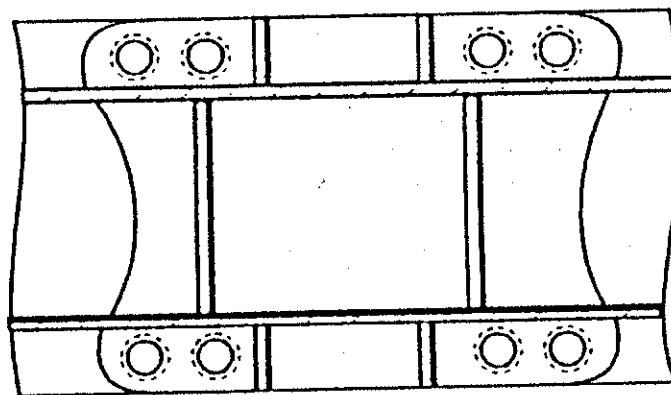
Контроль мест крепления подпятника (вид снизу)
